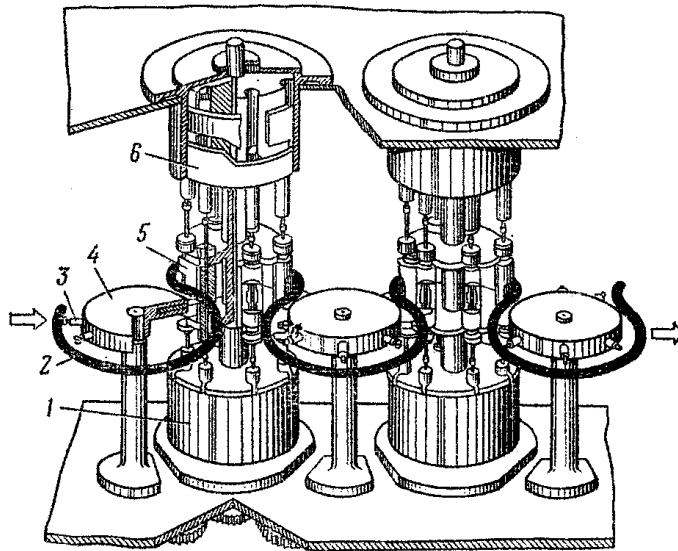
Група верстатів автоматичної роторної лінії: 1 – роторні верстати; 2 – шлях, який проходить оброблювана заготовка по верстатах і конвеєрній лінії; 3 – кліщі (захвати) транспортного ротору для захвату деталі, 4 – транспортувальні ротори для переміщення заготовок на роторні верстати; 5 – блок інструментів; 6 – копір для позовжнього (осьового) переміщення інструмента
